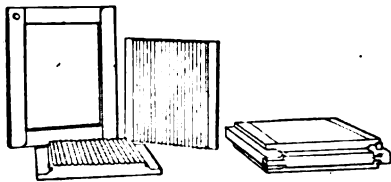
Moules en acier pour la fabrication des charbons à arc.
